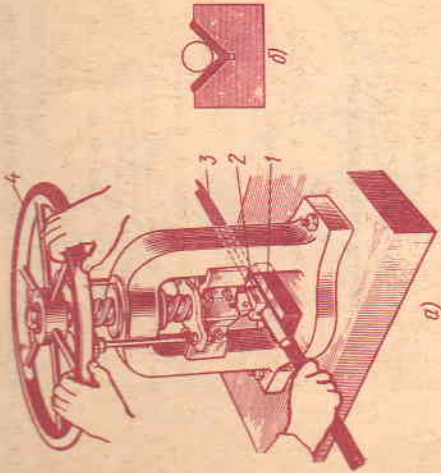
Правка уголка на ручном винтовом прессе: 1 — стол, 2 — призма, 3 — уголок, 4 — маховик
